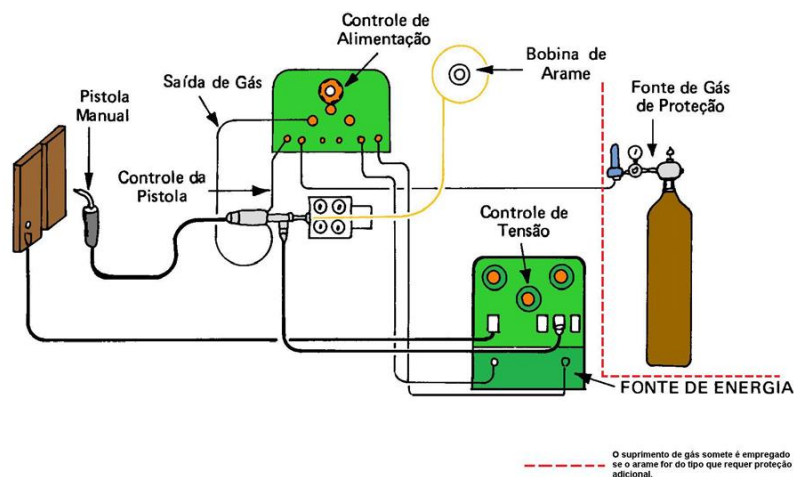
Esquema da montagem do equipamento para soldagem com Arame tubular.
